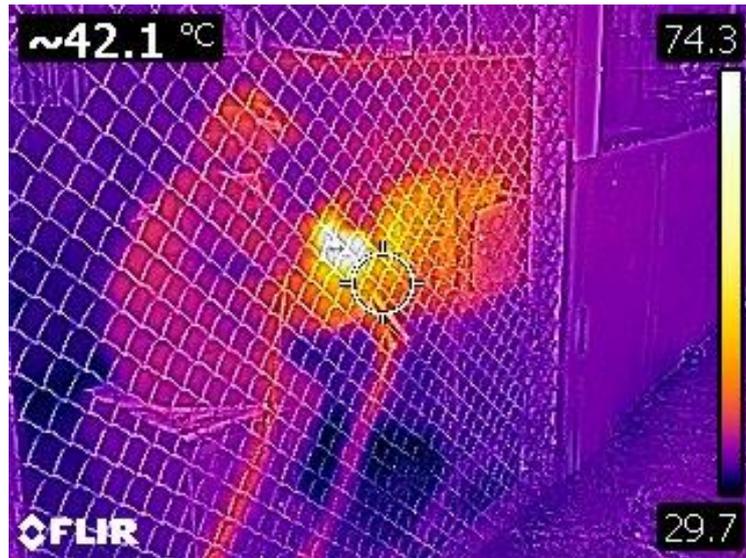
Fotografía termografica de uso de soldadora en el área de soldadura
